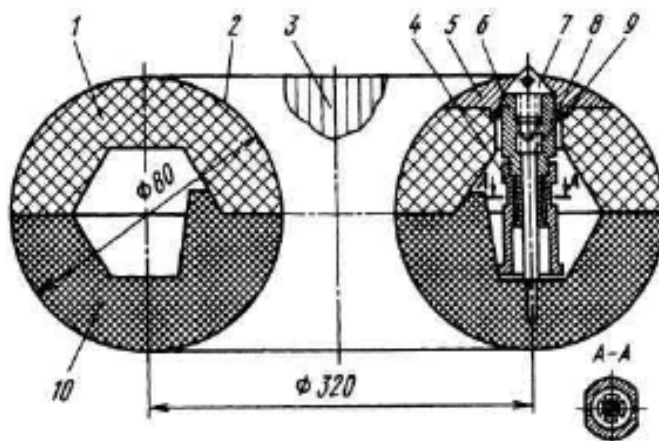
Конструктивная схема вымываемой песчаной оправки торовой формы с закладными элементами штуцера оболочки и цанговым устройством для извлечения штуцера из оправки после намотки однонаправленного КМ: 1, 10 - верхняя и нижняя половинки торовой оправки; 2 - поверхностный слой из пленки ПВС-Э; 3 - схема укладки ленты, вырезанной из пленки ПВС-Э; 4 - штуцер; 5 - втулка; 6 - разжимная цанга; 7 - раздвижной конус; 8 - фторопластовое уплотнение; 9 - установочный винт
